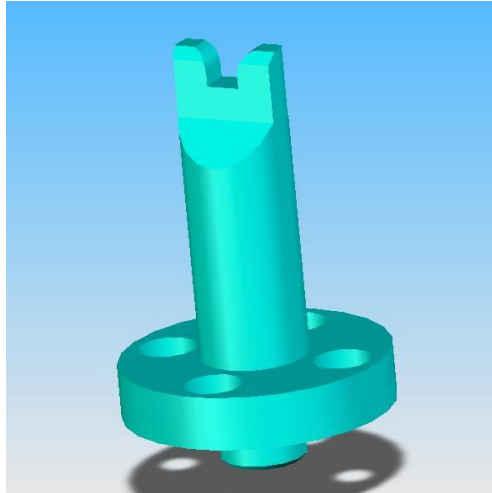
Apoio do ponto de ligação ao braço de direcção
